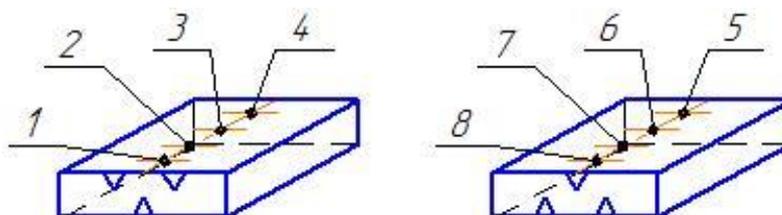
Исследуемый образец стали 12Х1МФ
